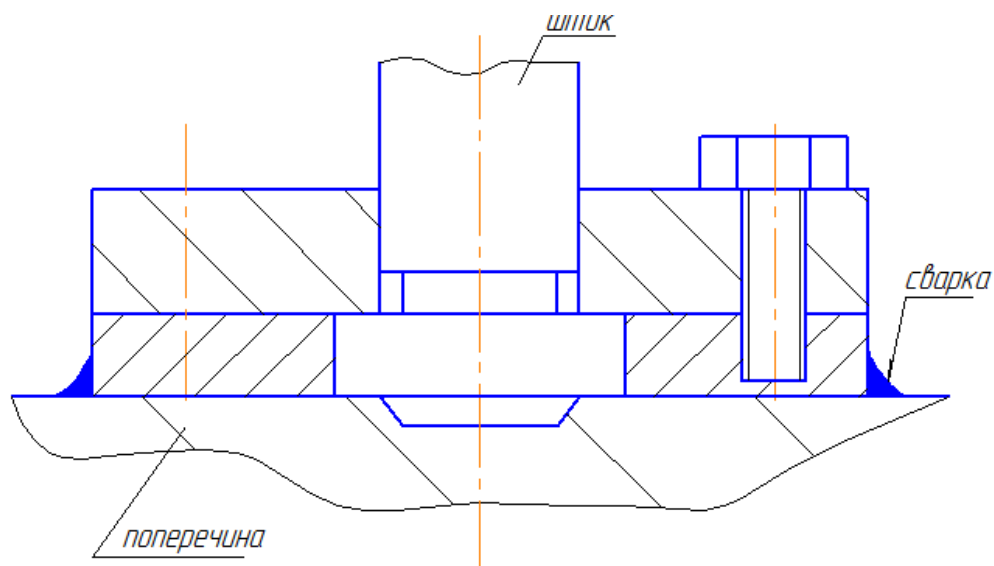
Соединение штока поршня цилиндра с поперечиной
